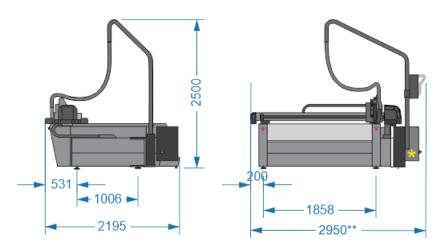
Grundriss rechte Seitenansicht und Vorderansicht
